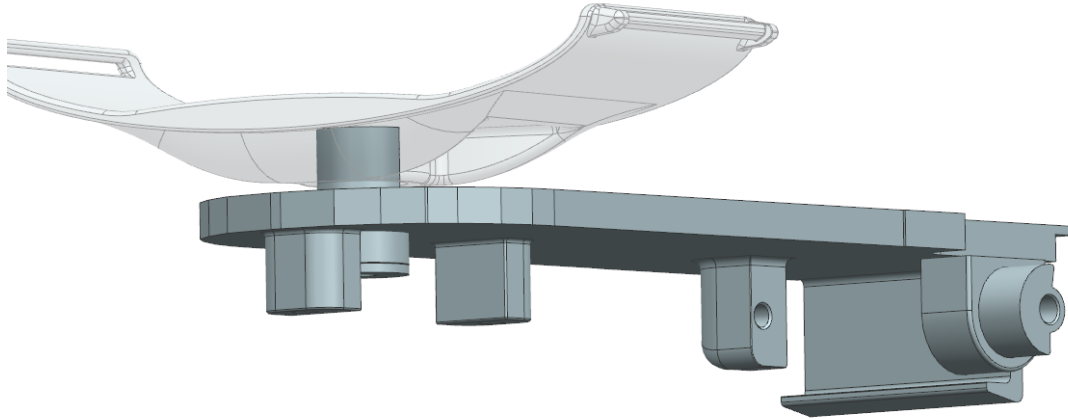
Diseño definitivo encaje soporte mano con placa; Fuente propia
